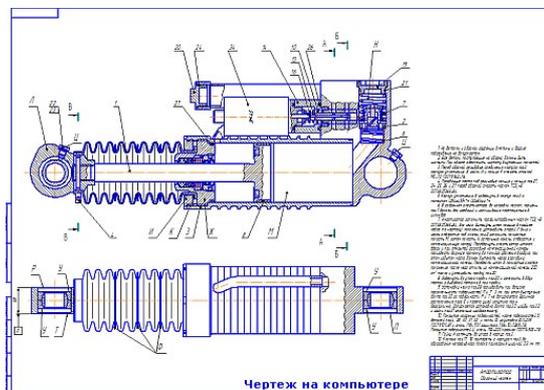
Современный чертеж, сделанный с использованием CAD систем
